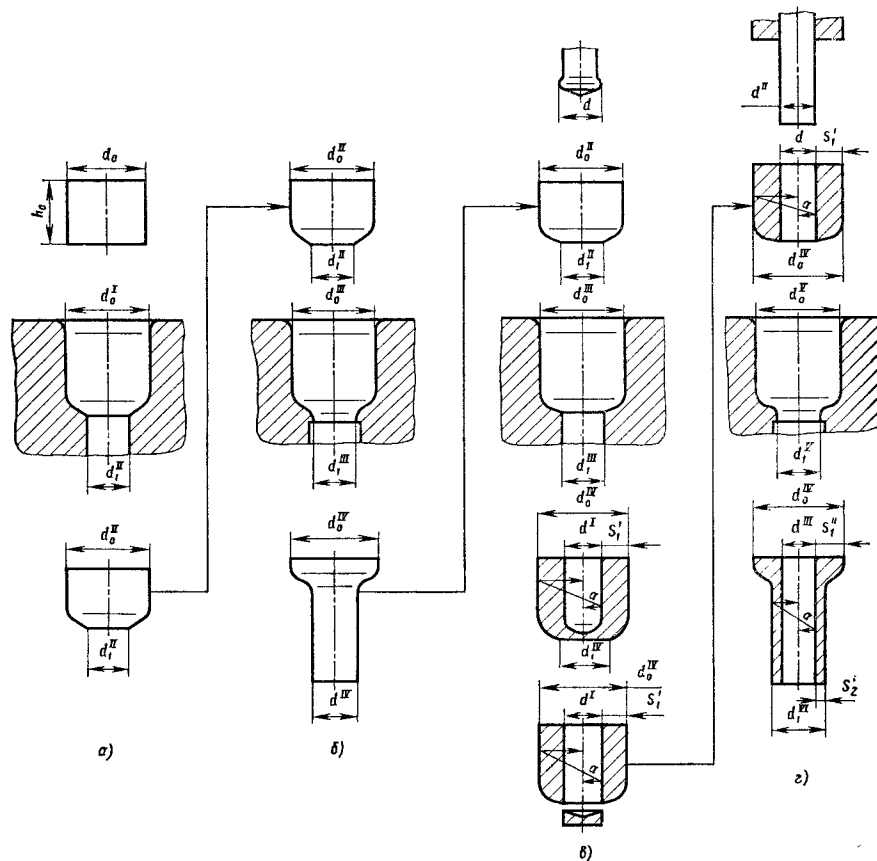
Схемы определения зазоров между заготовкой и инструментом при прямом и обратном выдавливании:
